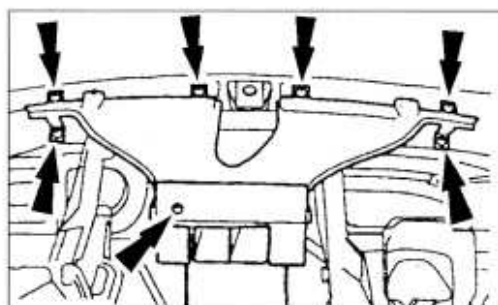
Śruby mocujące skrzynkę bezpieczników
